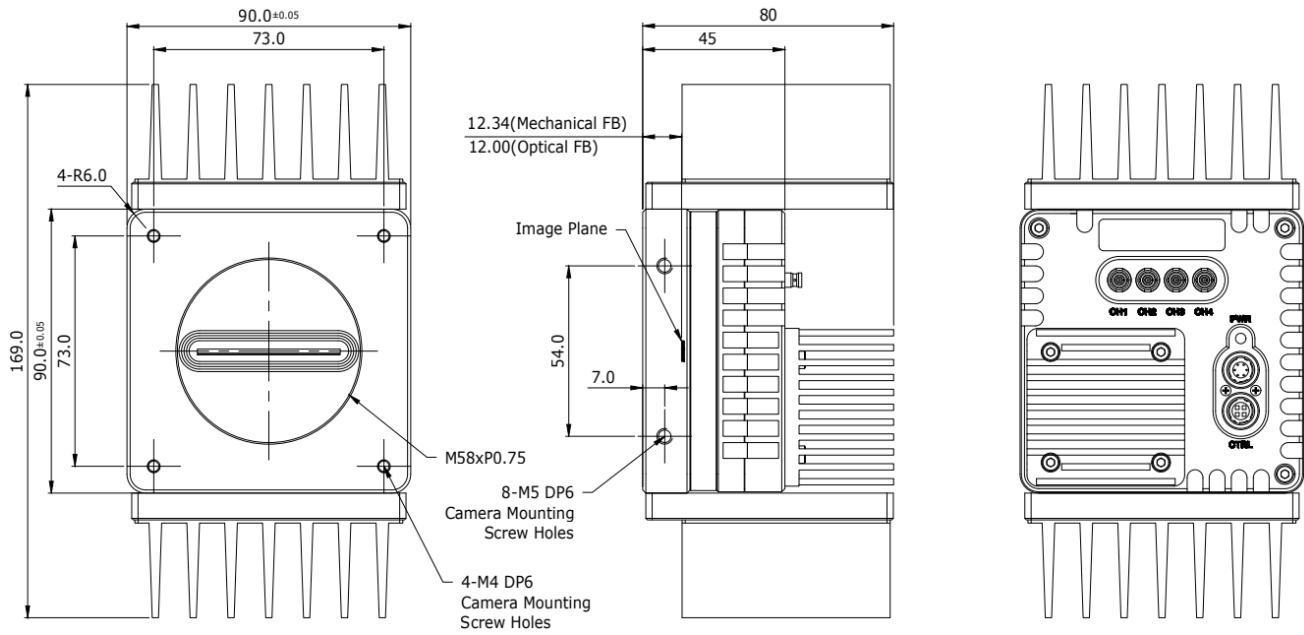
VTS-9K5X2 Mechanical Dimension (with Heatsink)
